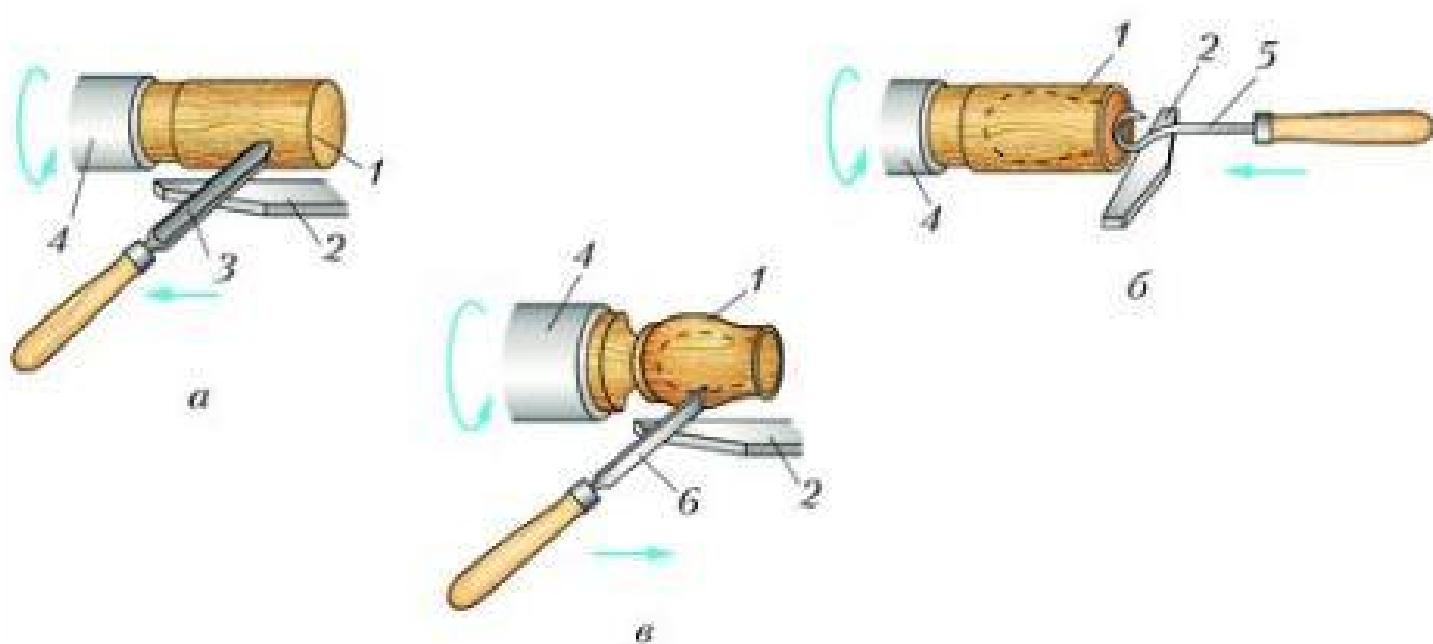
Обработка заготовки, установленной в патроне станка: а – черновое точение; б – растачивание внутренней полости; в – чистовая обработка наружной поверхности; 1 – заготовка; 2 – подручник; 3 – полукруглая стамеска; 4 – патрон; 5 – крючок; 6 – мейсель
